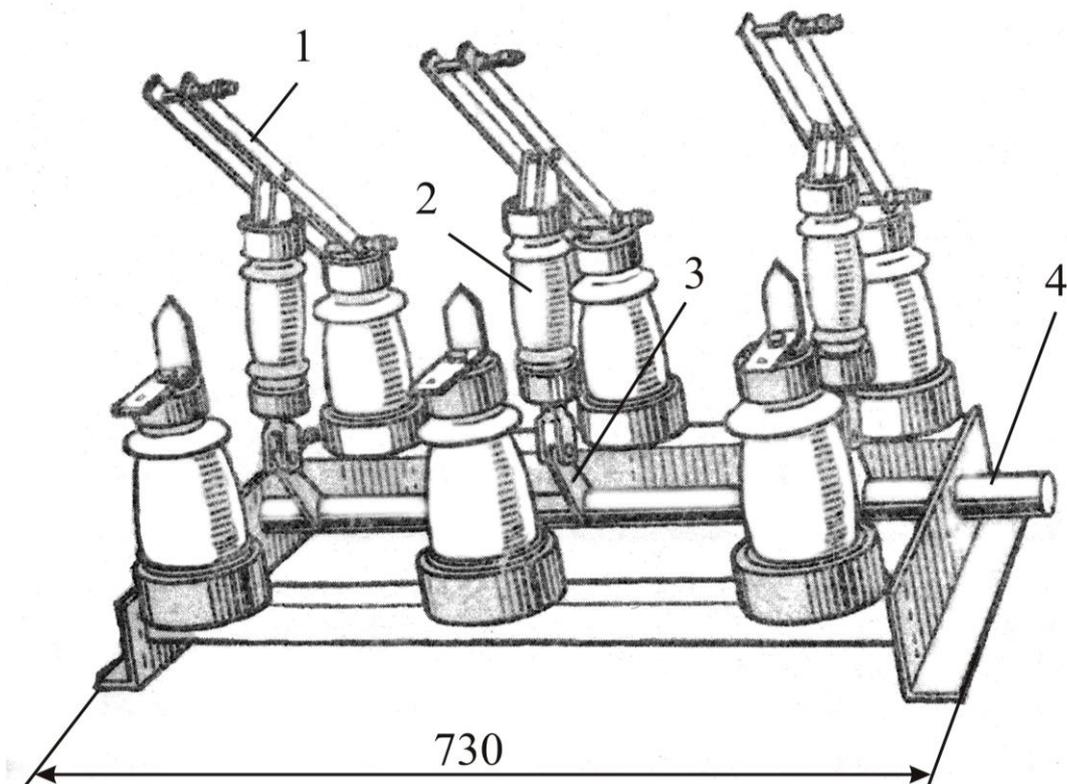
Разъединитель типа РВ-10/400:
